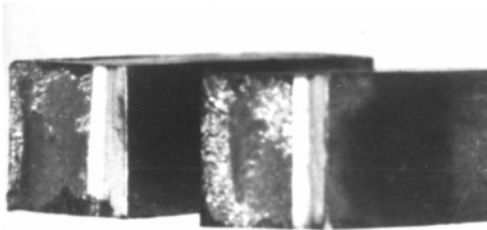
Характер руйнування зразка зварного з'єднання при випробуваннях
